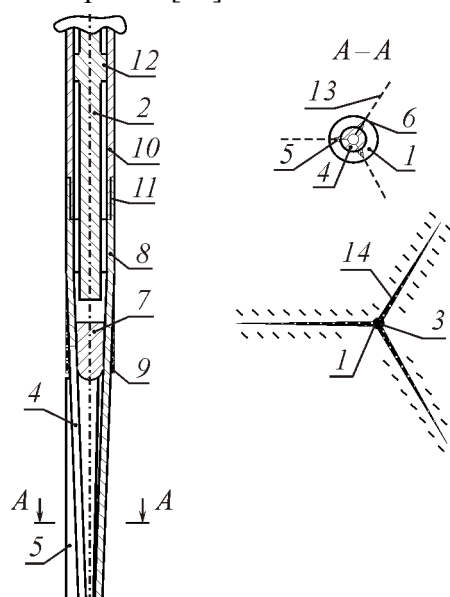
Схема одновременного формирования трех продольных трещин: 1 — скважина; 2 — штанга; 3 — флюид; 4 — лепестки цанги; 5 — клинья; 6 — смыкание клиньев; 7 — наковальня; 8 — цанга; 9 — эластичная втулка; 10 — труба; 11 — резьба; 12 — кольцевой выступ; 13 — плоскость разрыва; 14 — трещина; A-A — разрез
